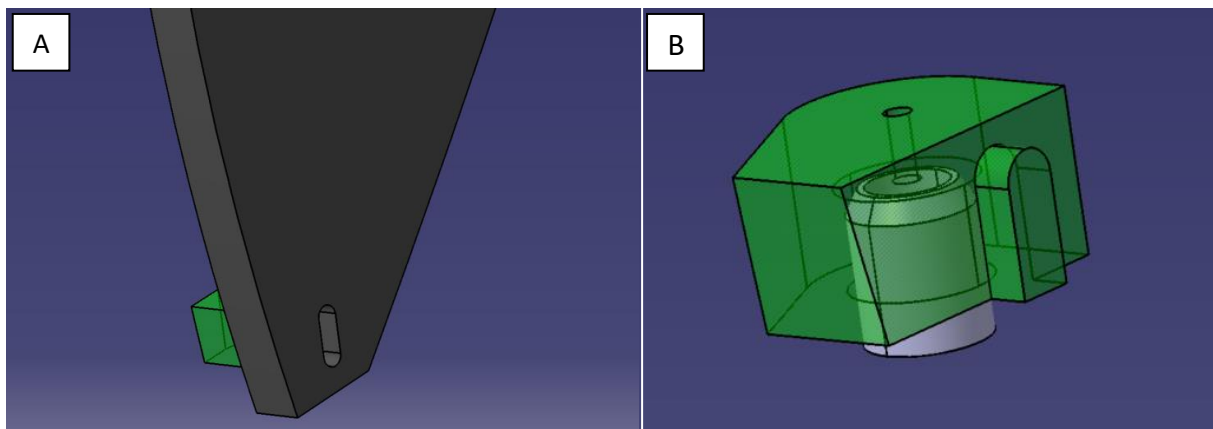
Bild A: Spant mit gefrästem Ausschnitt für die Positionierung der Bolzenhalterung; Bild B: Bolzenhalterung (grün) mit Positionierungsgeometrie, die dem Ausschnitt im Hauptspant entspricht.
